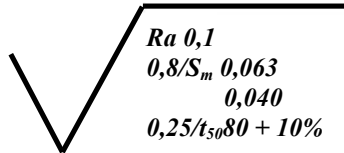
Обозначение шероховатости при двух и более параметрах
